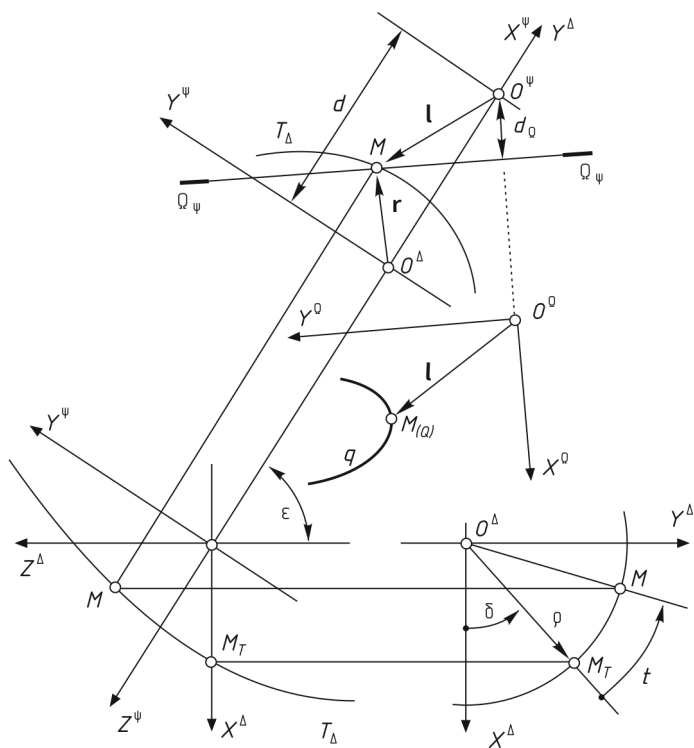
Рухомя площина, як передня поверхня зубця фрези
